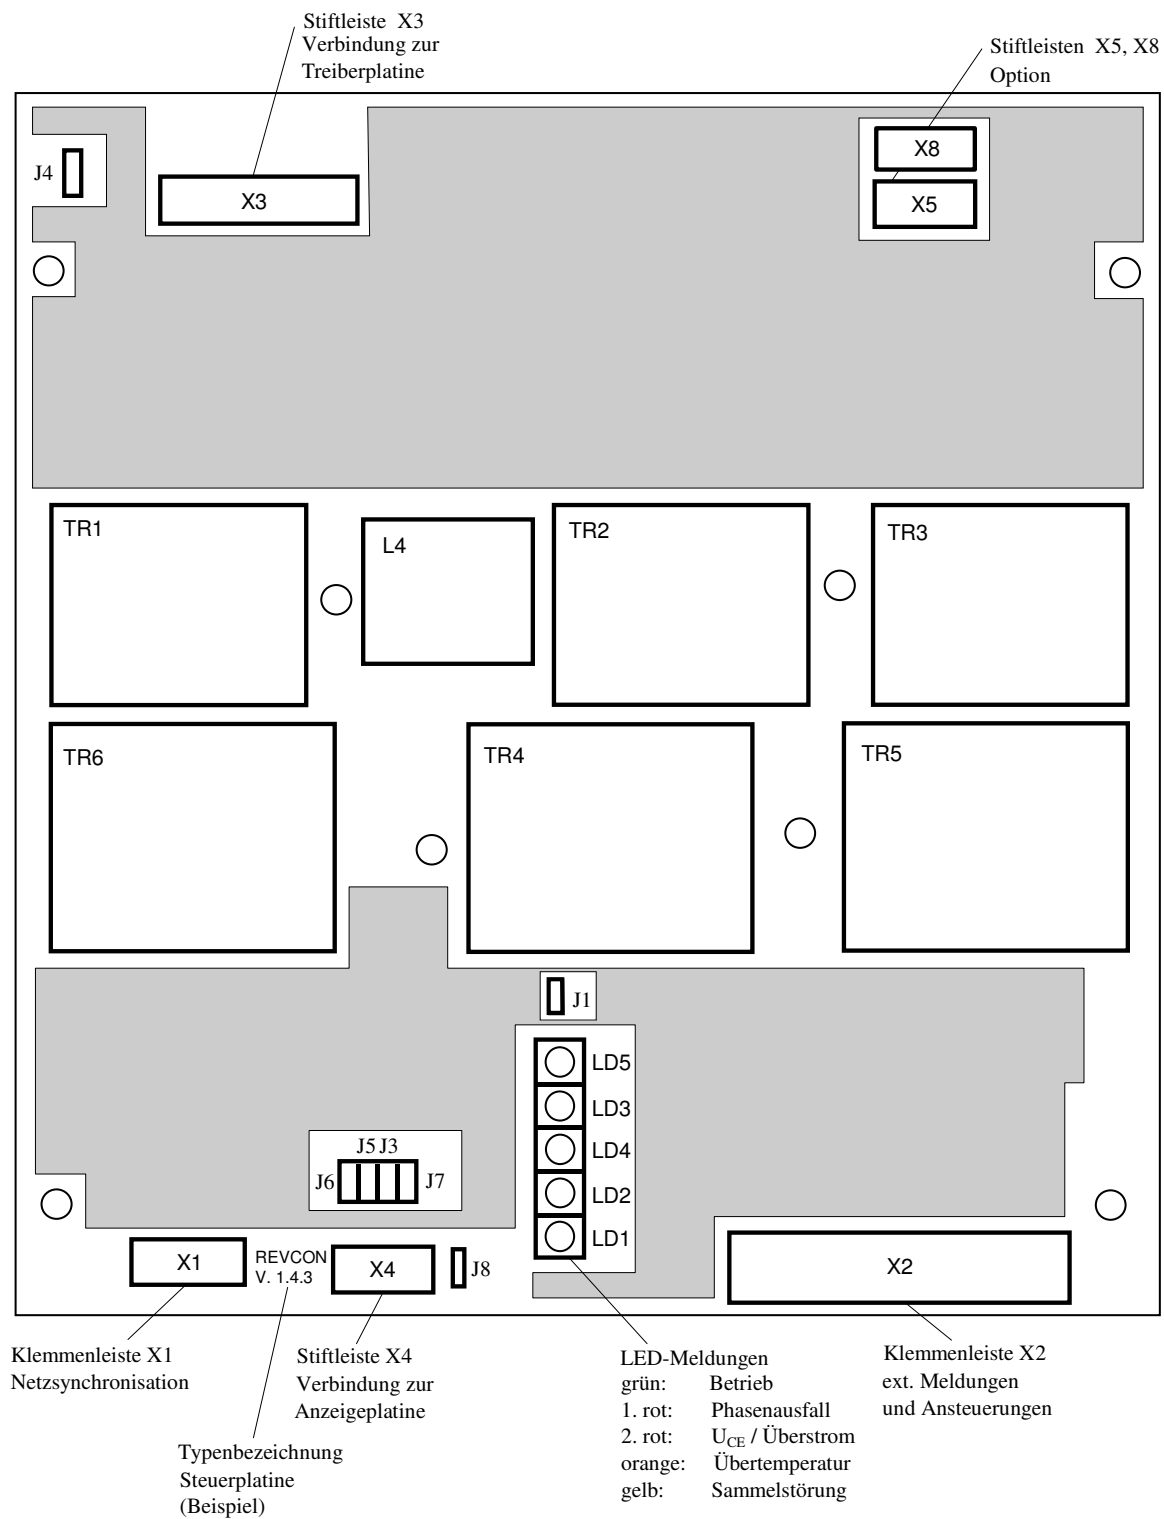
Anschluss- und Bauteile-Lageplan der SVCD-Steu Platine REVCON 1.4.4
